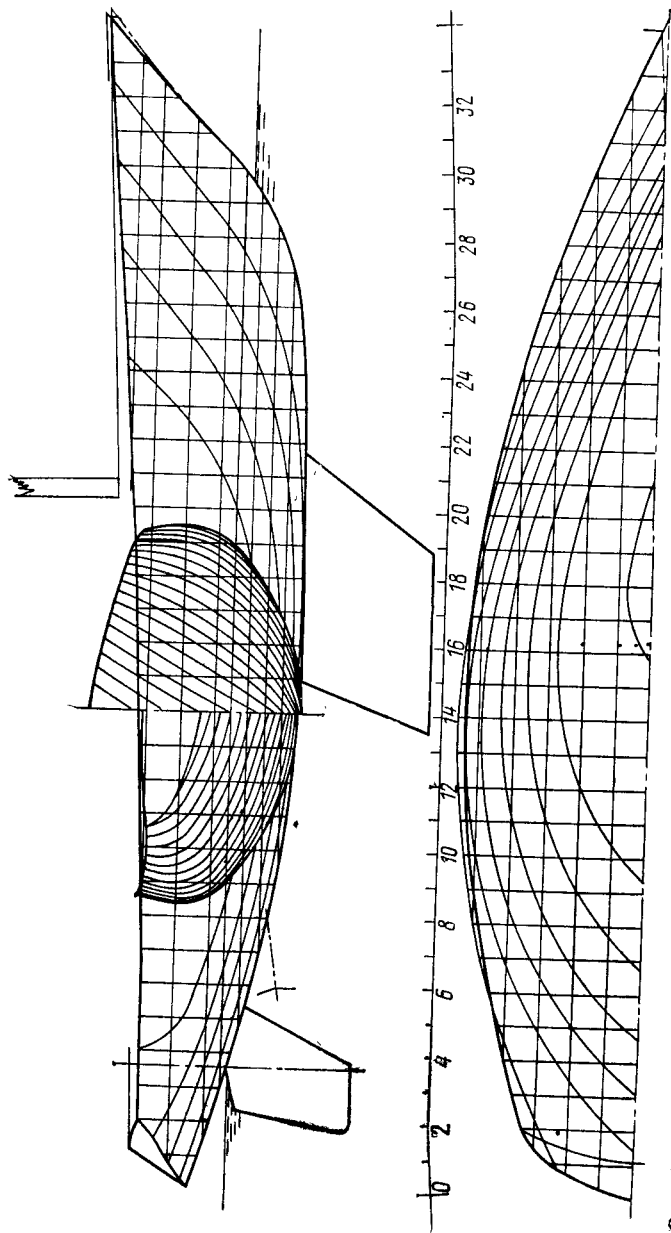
Теоретический чертеж яхты «Гласер-34».
